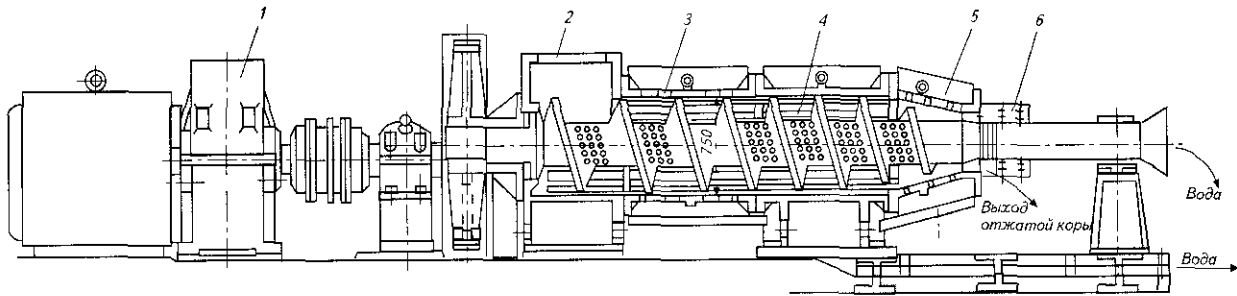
Общий вид винтового пресса с цилиндрическим винтом диаметром 750 мм:
